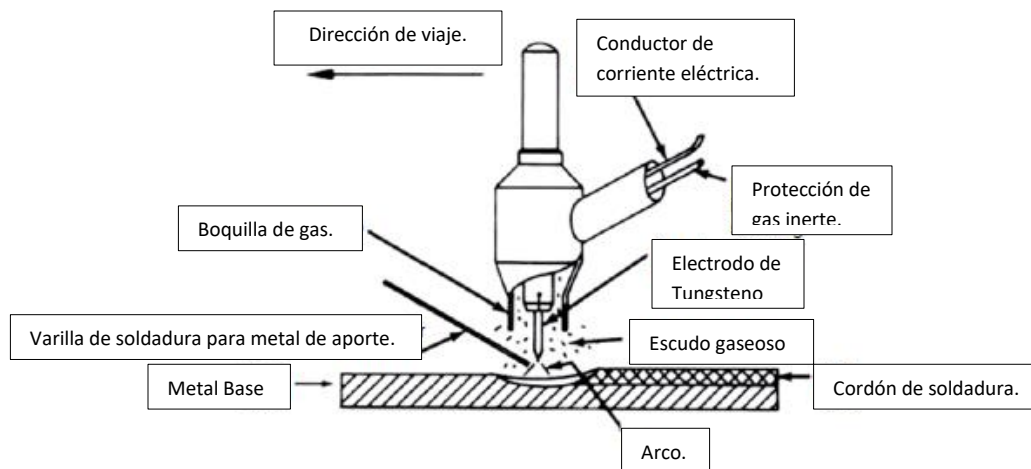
Soldadura por arco de tungsteno con gas. [30]
